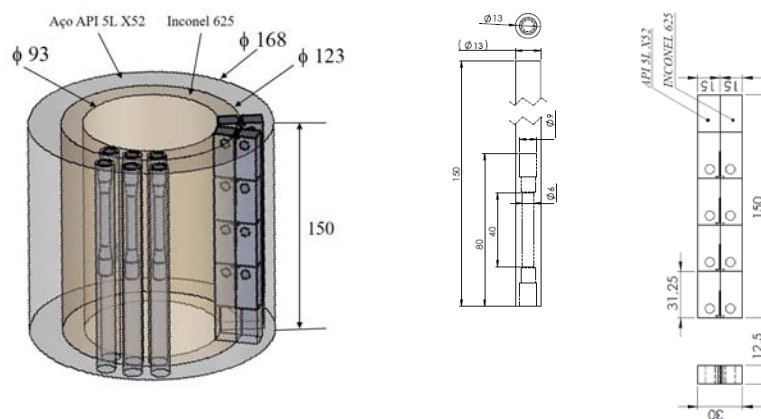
Layout de usinagem da amostra tubular e dimensões normalizadas dos corpos de prova.
